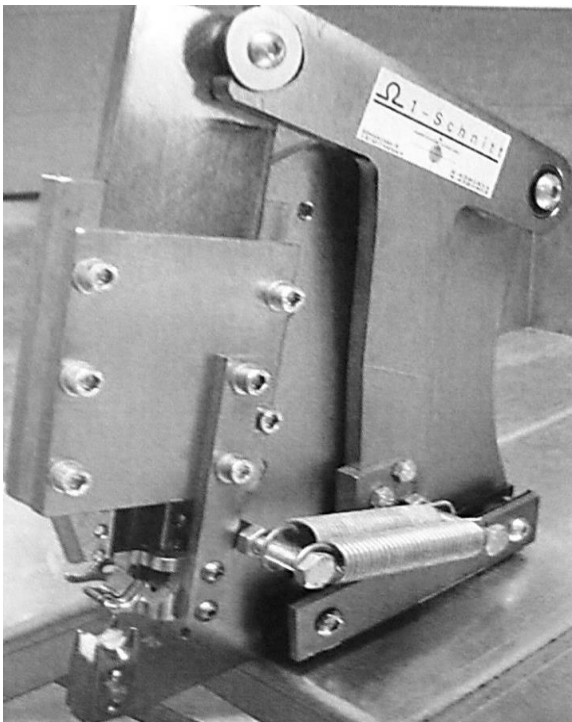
Щеплювальний пристрій «1 - cut» фірми WAGNER
